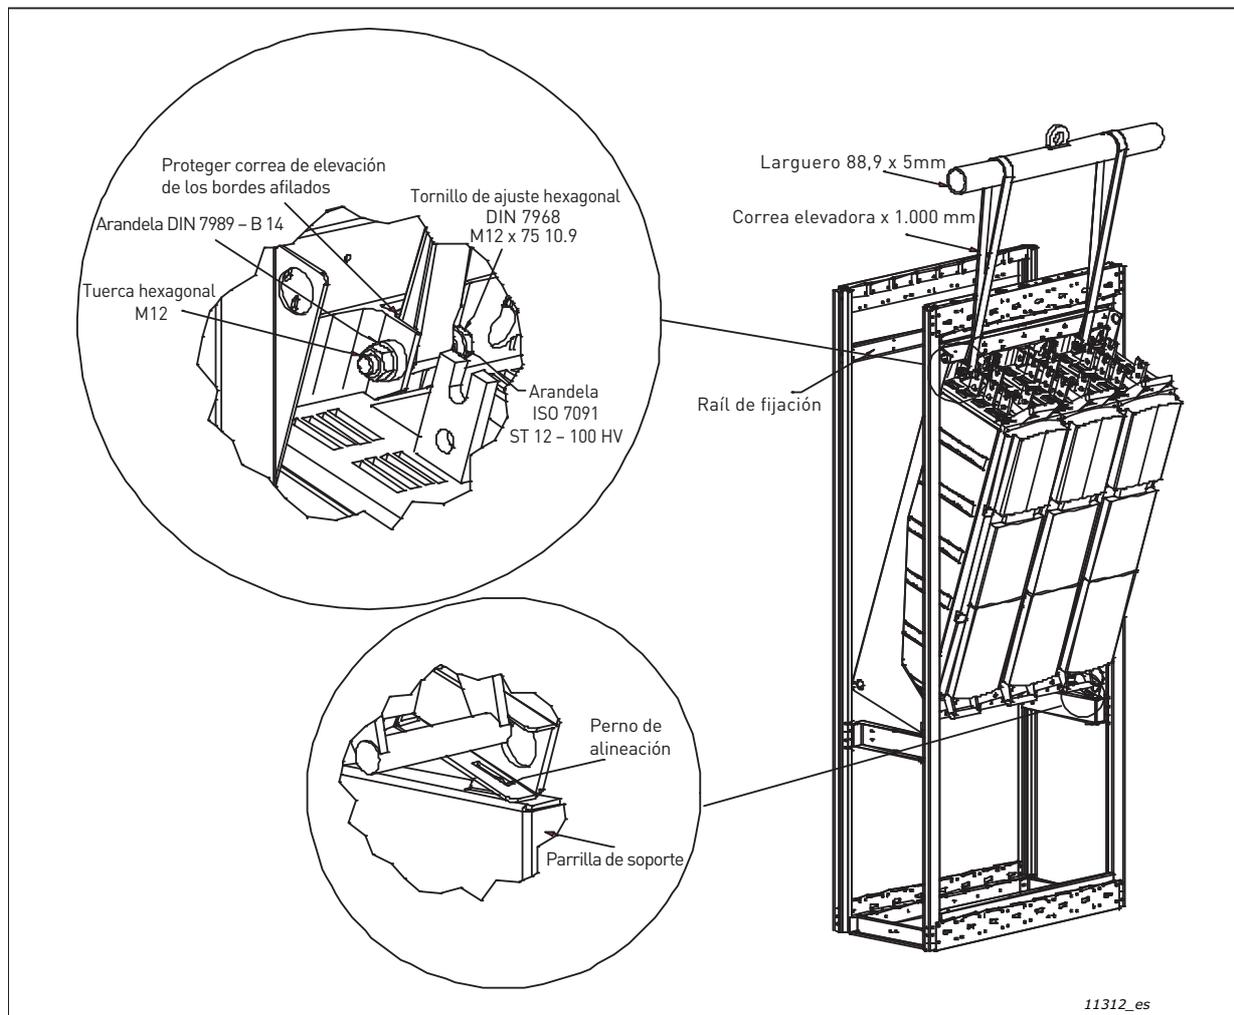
Elevación del convertidor en un espacio de montaje estrecho
